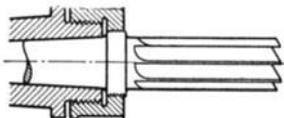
Fräserbefestigung durch Ausgleichsgewinde.
